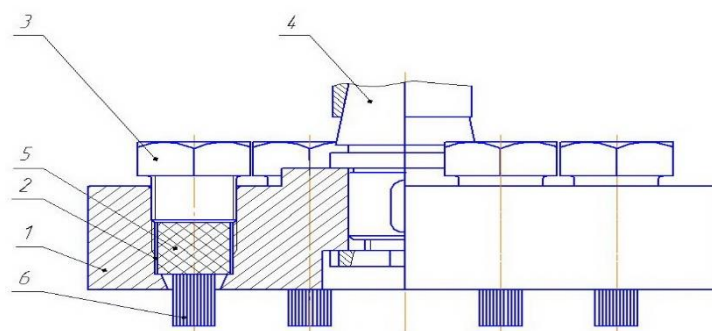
Торцевая иглофрезасборной конструкции со вставными режущими элементами: 1- цельный корпус иглофрезы, 2 - «сквозное» установочное отверстие для замены режущего элемента (держателя ворса), 3 - болт для фиксации режущего элемента (держателя ворса), 4 - приводная оправка иглофрезы в шпиндельном узле станка, 5 - сменный блок режущего элемента (держатель ворса), 6 - проволочный ворс (иглы).
